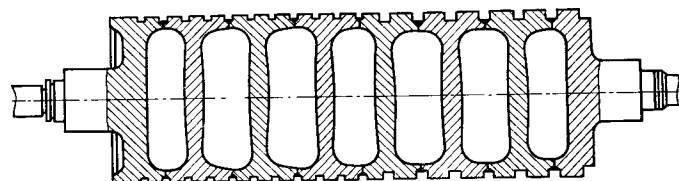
Сварной ротор осевого компрессора ГТУ фирмы Броун — Бовери
